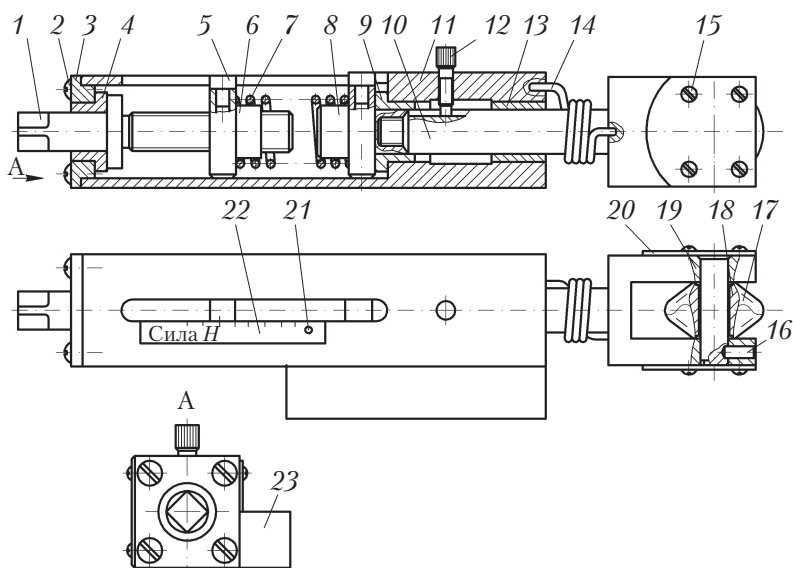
Приспособление со сменными головками, оснащенными профильными роликами
